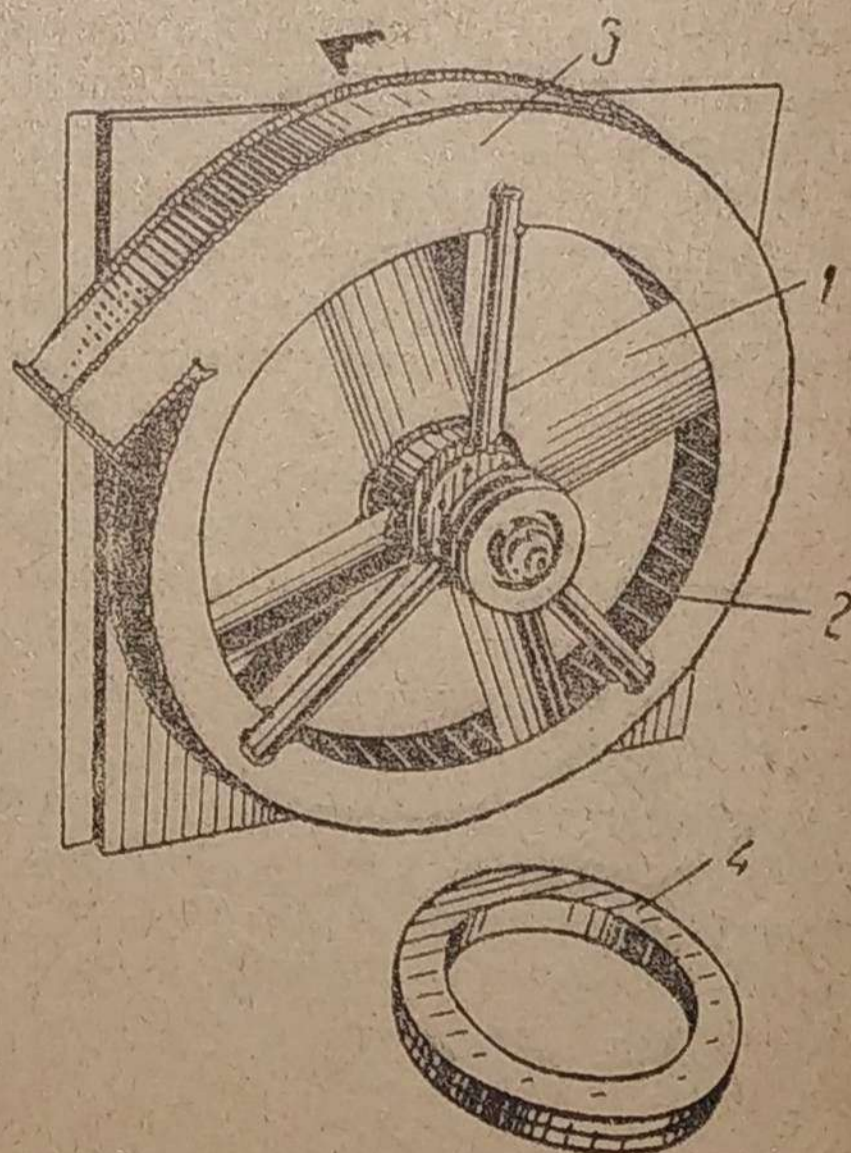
Опытный образец воздуходувки к двигателю ХТЗ
